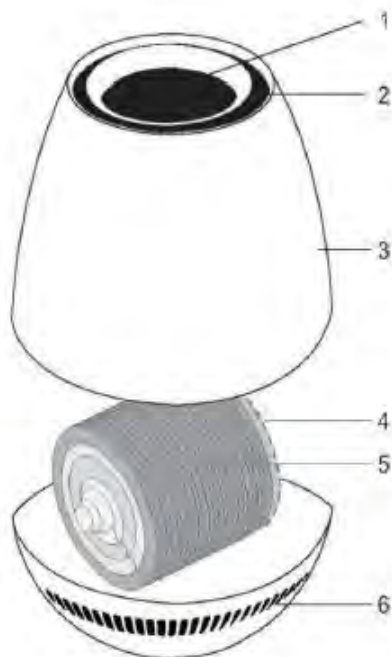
Конструкция мойки воздуха: 1 – панель управления, место долива воды 2 – внутренняя конструктивная поддержка корпуса, 3 – корпус изделия, 4 – водное колесо, 5 – диски водного колеса, 6 – водный резервуар.
